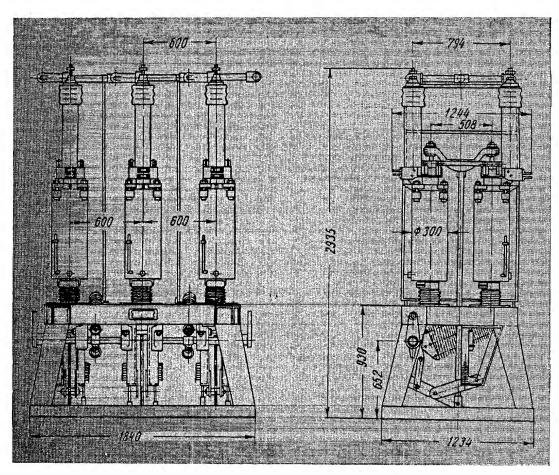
Габаритные размеры выключателя типа МГГ-229М.
